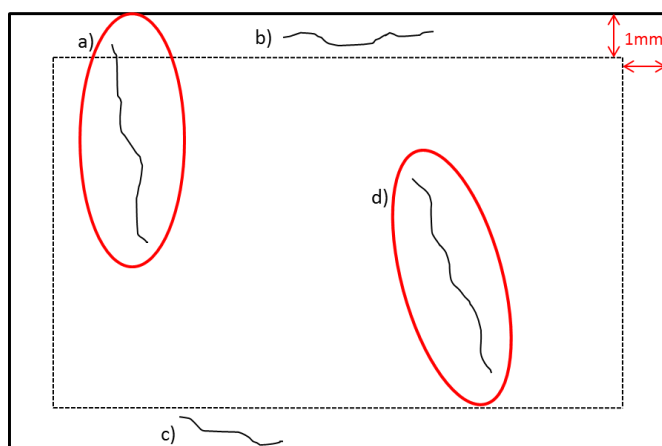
Exemplo de fissuras no corpo de prova.
